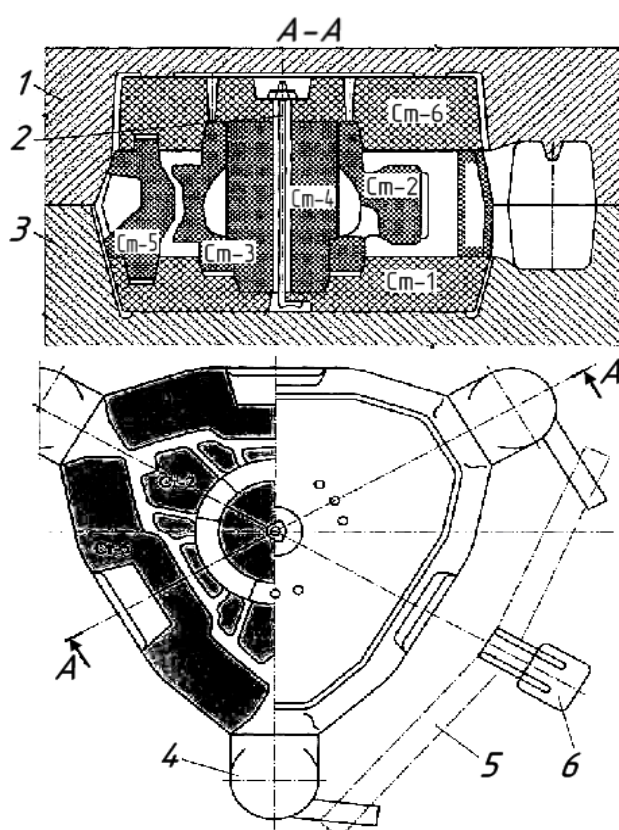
Формовка в стержнях: 1- верхняя полуформа; 2- шпилька; 3- нижняя полуформа; 4 - прибыль; 5 - литниковый ход; 6- дроссель; Ст1 - Ст 6 - стержни.
